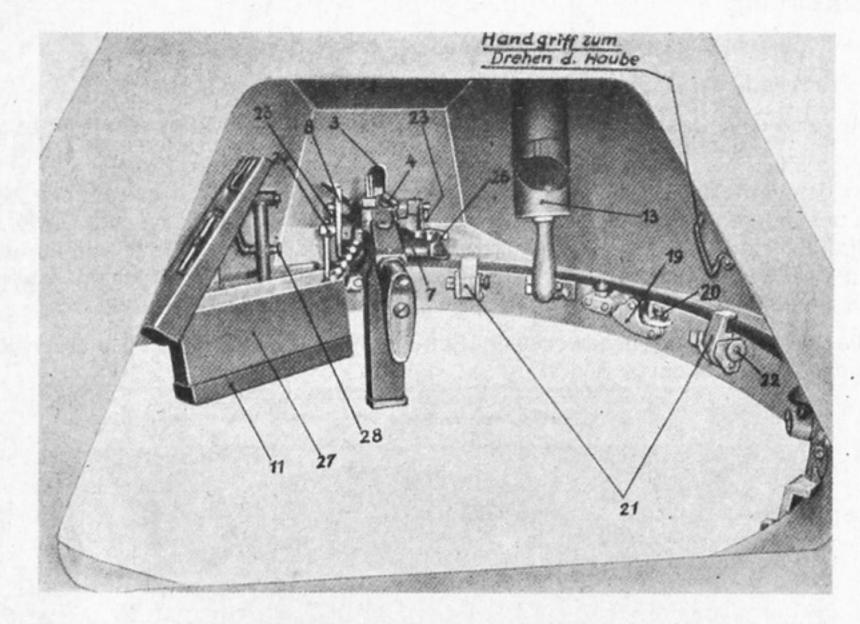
Innenansicht der Drehhaube 4007 durch die Einstiegluke
